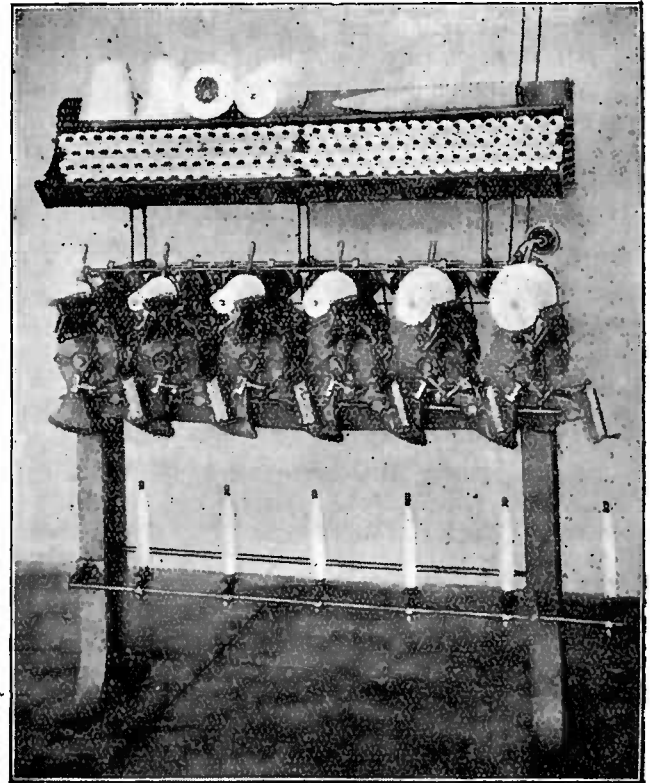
Bobinoir • Universal Winding • bobine conique.
